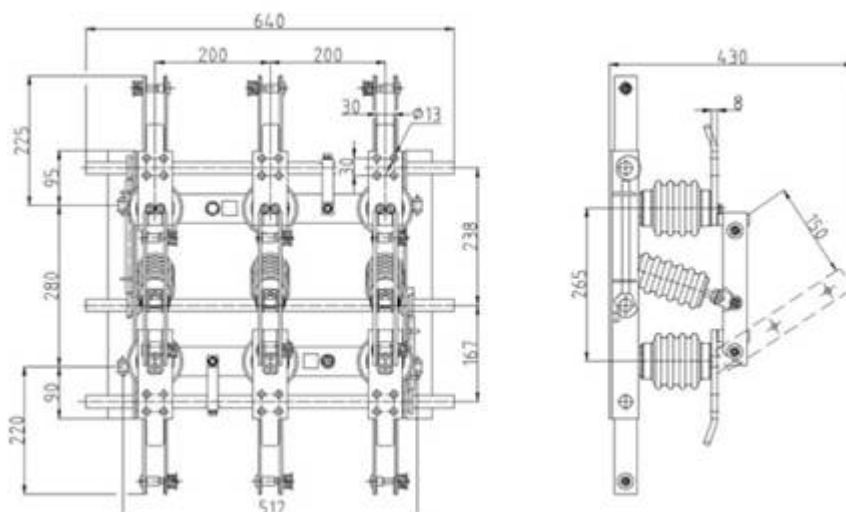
Разъединитель типа РВ-10/400-1 УЗ
